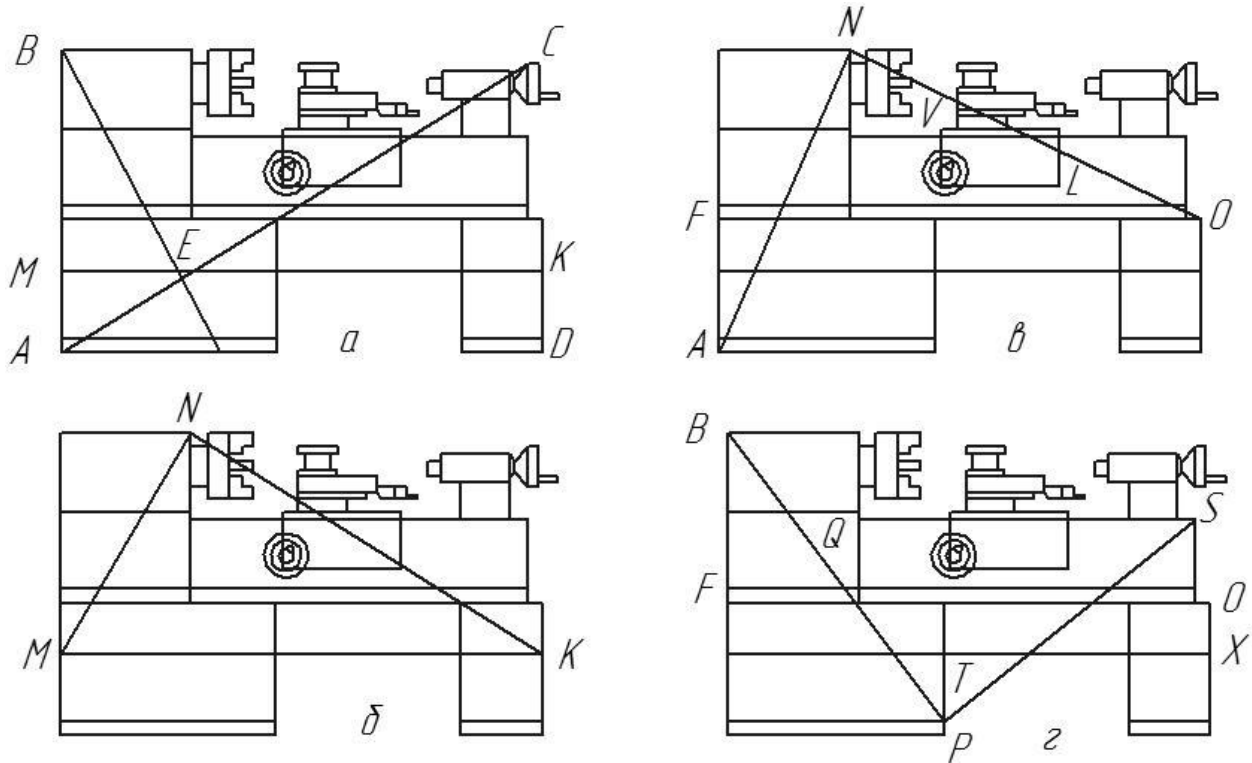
Схеми пропорціонування токарно-гвинторізного верстата
